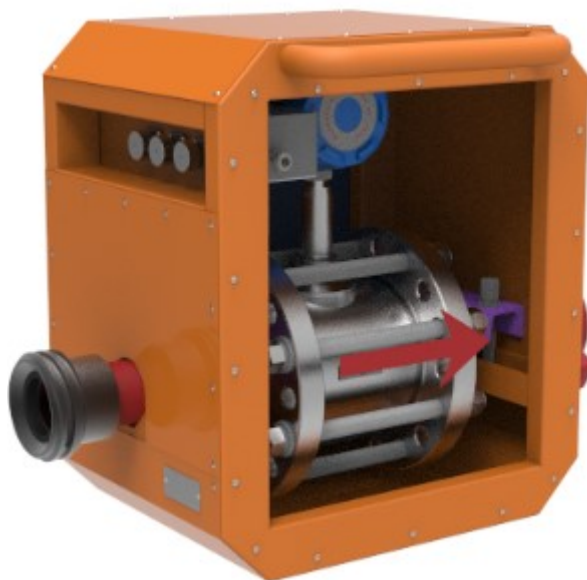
Внешний вид ДР-150 (боковая стенка условно не показана)
